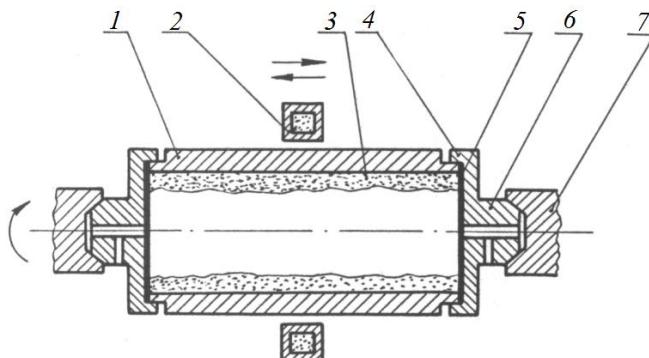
Схема нанесення евтектичного покриття на внутрішню поверхню циліндричної деталі з використанням нагрівання СВЧ: 1 – стальна втулка; 2 – індуктор; 3 – шихта; 4 – фланець; 5 – ущільнення; 6 – отвори для виходу газів; 7 – зворотній центр
